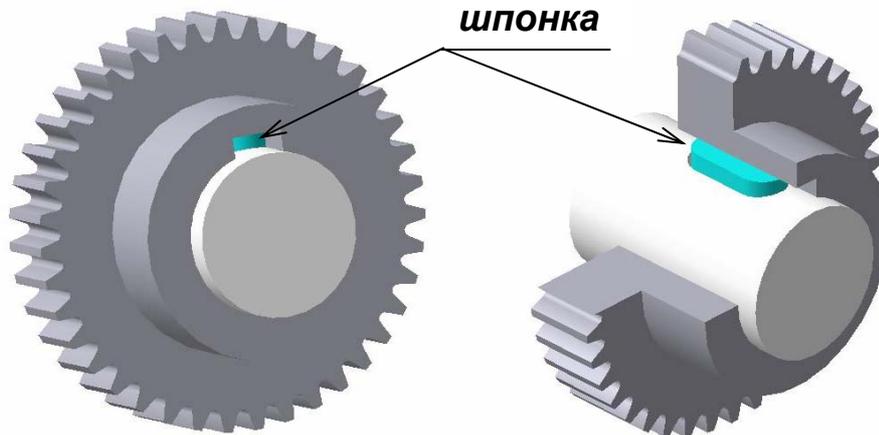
Шпоночное соединение зубчатого колеса с валом
